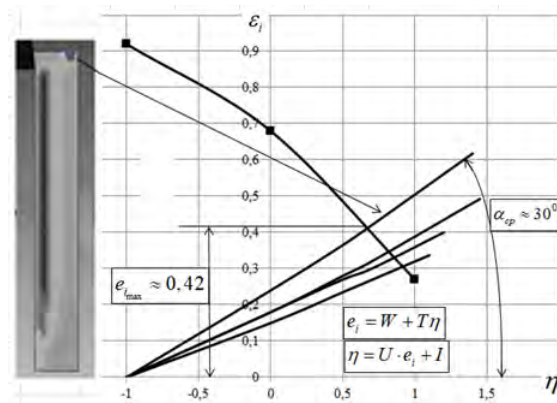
Шляхи деформування, що характерні для небезпечної точки заготовки при фіксованому натягові заготовок із сплаву W-Ni-Fe при різних значеннях кута нахилу матриці.
